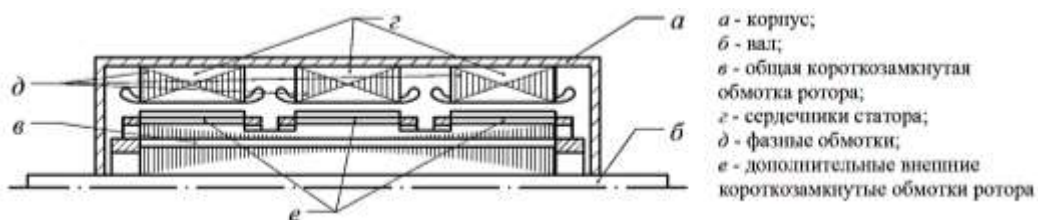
Конструктивная схема многостаторного асинхронного двигателя с дополнительными короткозамкнутыми обмотками
